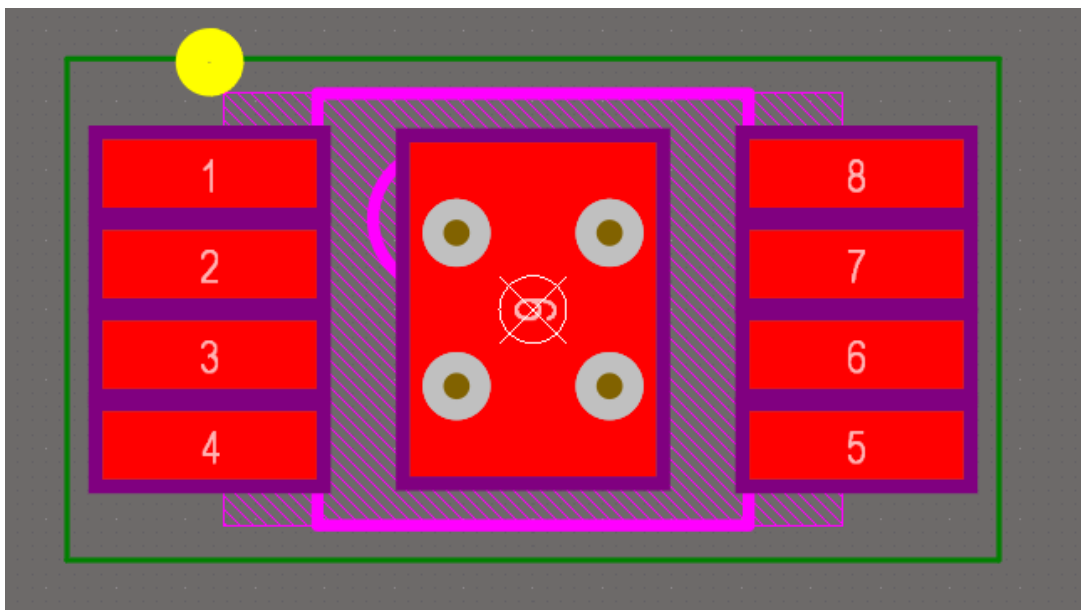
Οδηγός δημιουργίας footprint (9)
